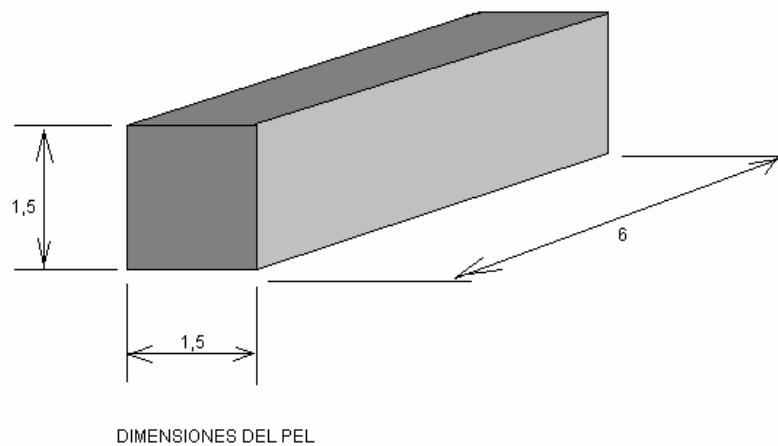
Dimensionado en mm del pellet en el nivel 2.
